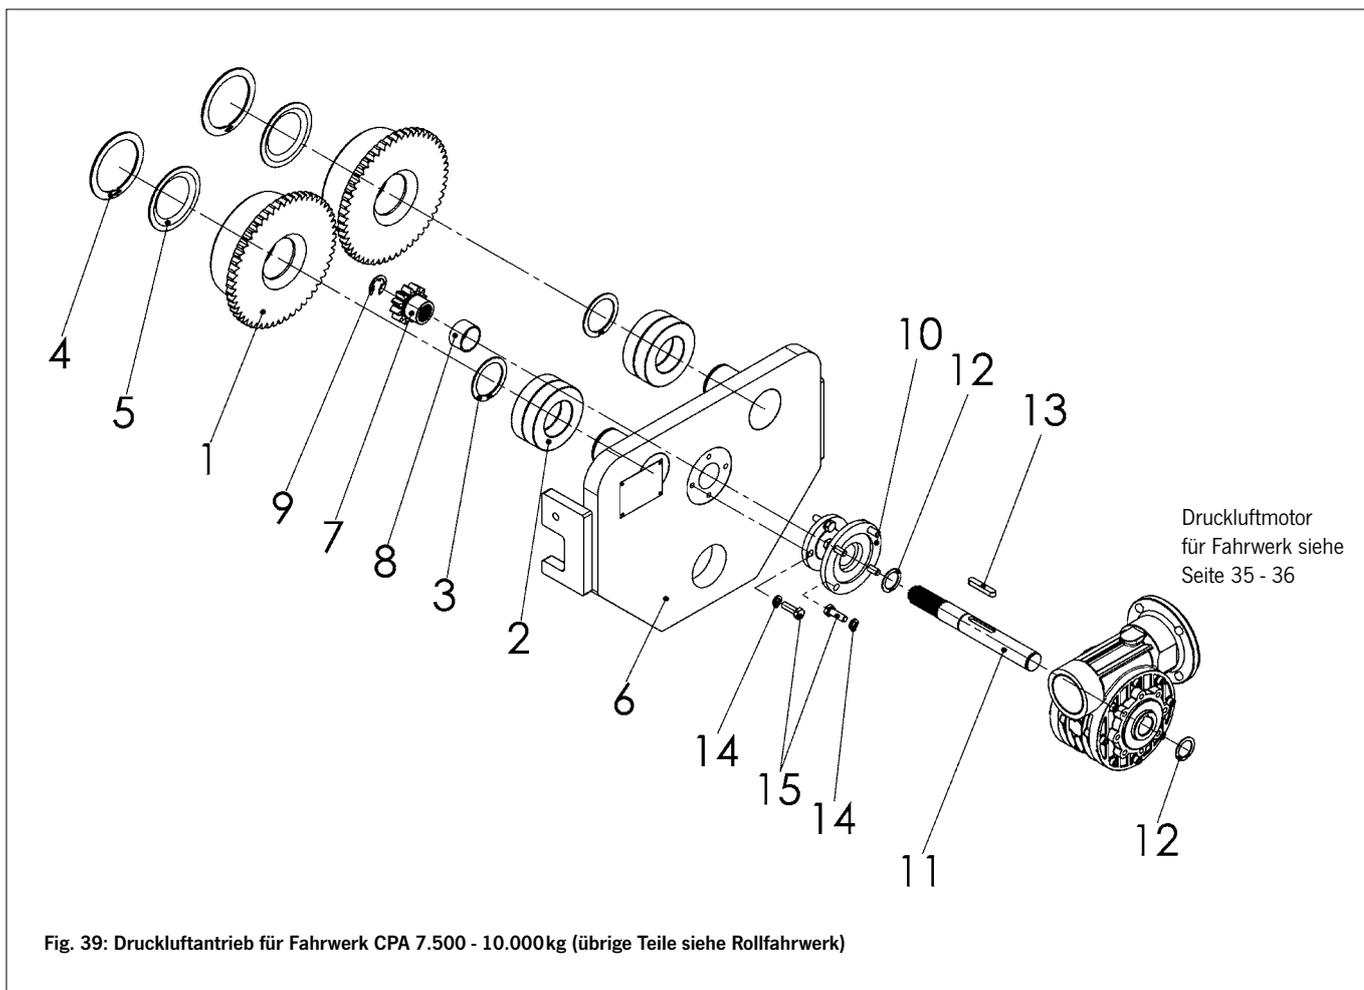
Druckluftantrieb für Fahrwerk CPA 7.500 - 10.000kg (übrige Teile siehe Rollfahrwerk)
